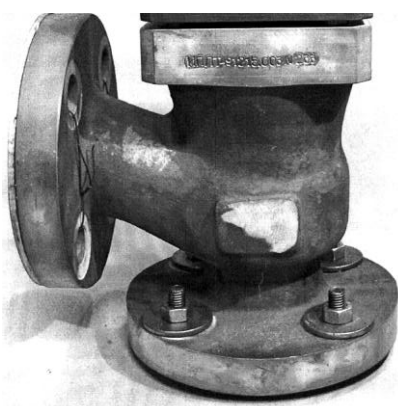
Фотография корпуса запорно-регулирующей арматуры.
